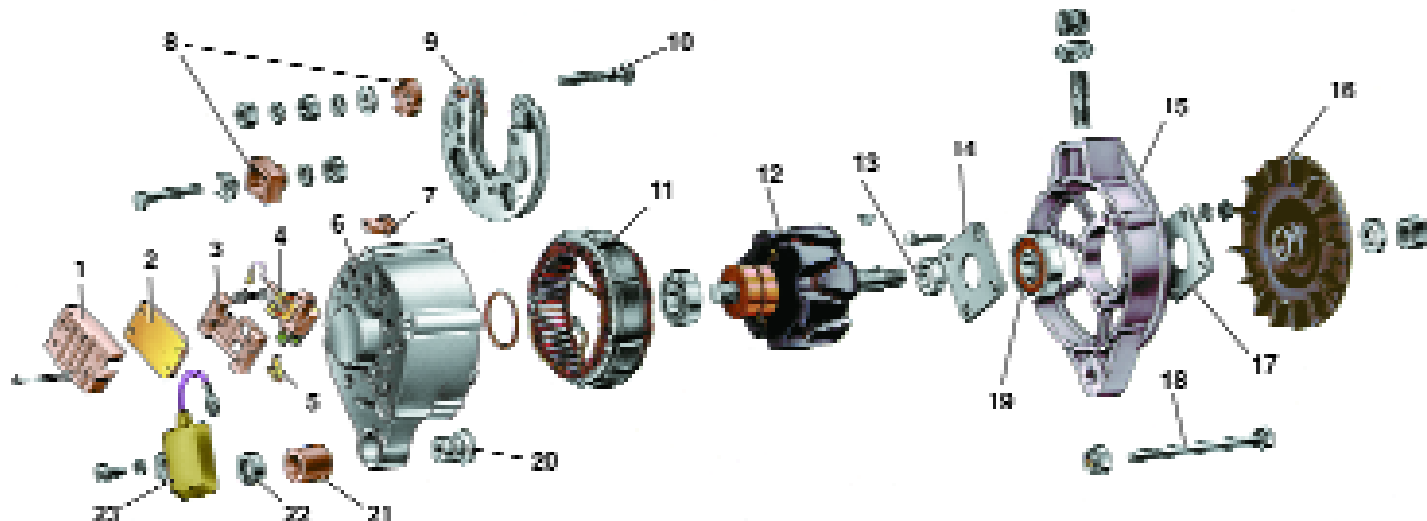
Детали генератора Г–222: 1 – кожух; 2 – регулятор напряжения; 3 – основание; 4 – щеткодержатель с щетками; 5 – вывод «15» генератора (вывод «Б» регулятора напряжения); 6 – крышка генератора со стороны контактных колец; 7 – колодка штекера центрального вывода обмотки статора; 8 – изолирующие втулки; 9 – выпрямительный блок; 10 – контактный болт;
